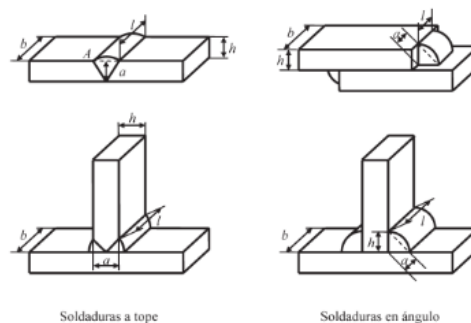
Uniones soldadas a tope y ángulo [41]
